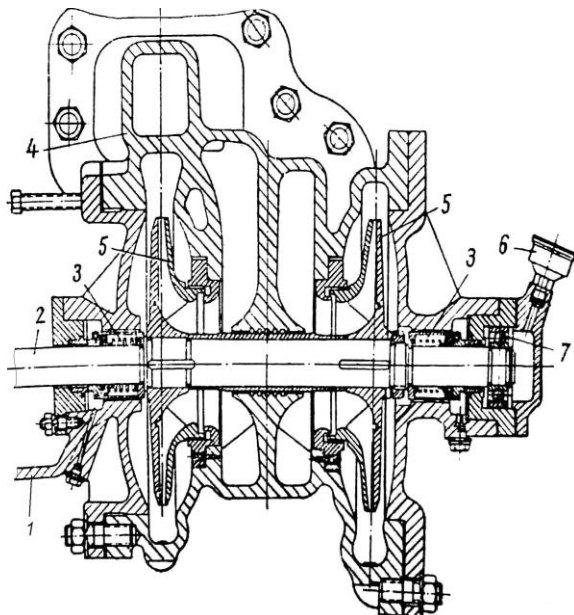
Насос ЦСП-57: 1 – опорный узел; 2 – вал; 3 – уплотнительные узлы; 4 – корпус; 5 – рабочее колесо; 6 – устройство для смазки (пресс-масленка); 7 – шарикоподшипник.
